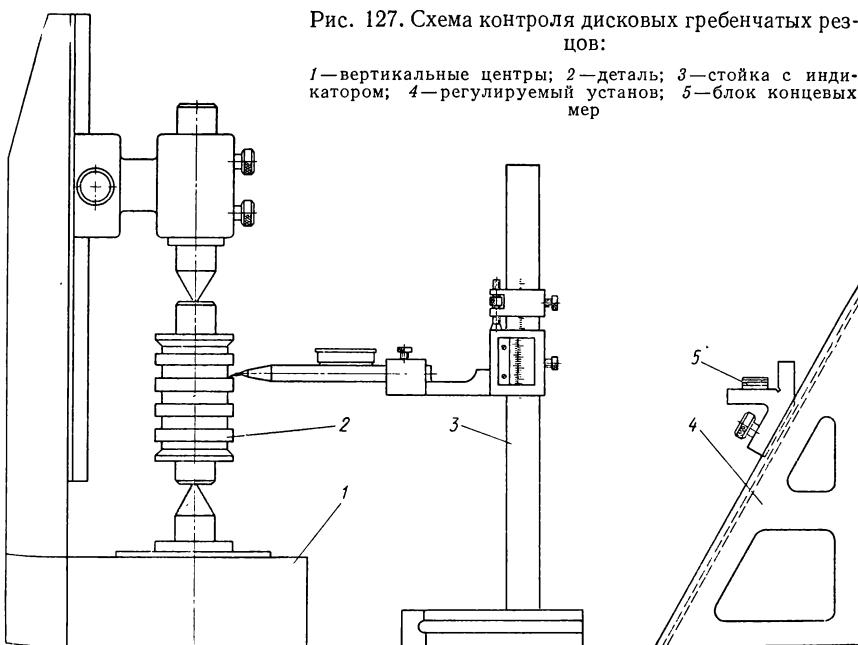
Схема контроля дисковых гребенчатых резцов:
